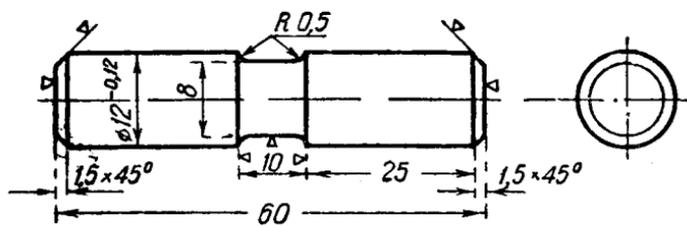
Дет. 04-23. Палец пусковой рукоятки
